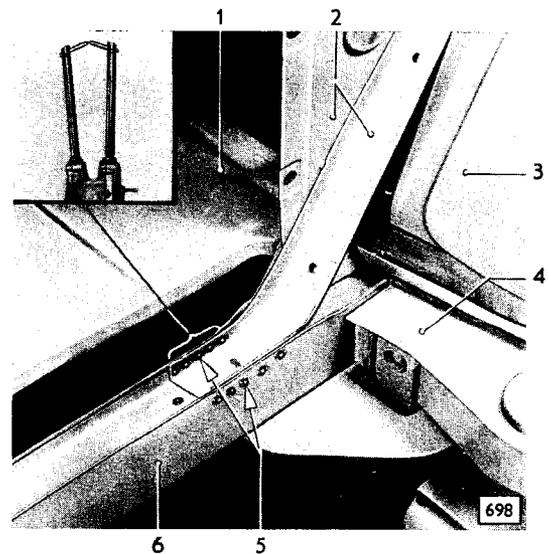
Stützwinkel der seitlichen Luftleitbleche an Vorderrahmenquerträger punktgeschweißt – Bild zeigt rechte Wagenseite
